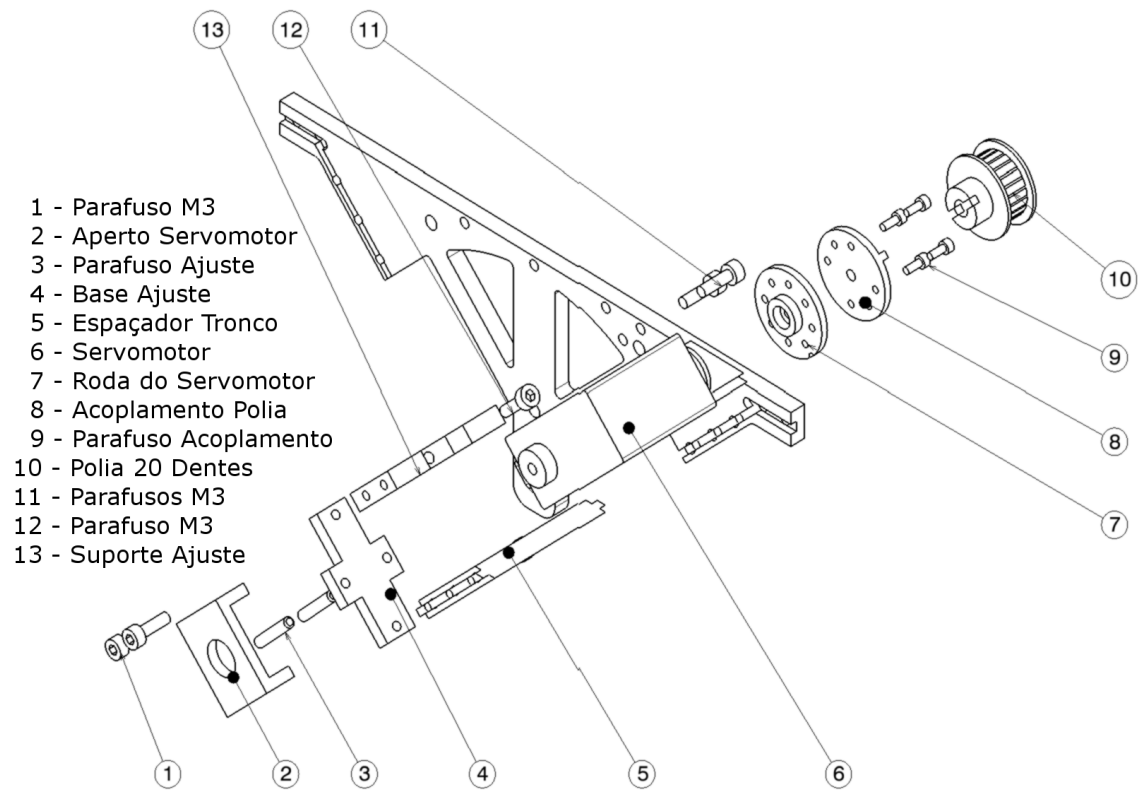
Vista explodida do actuador para inclinação lateral.
